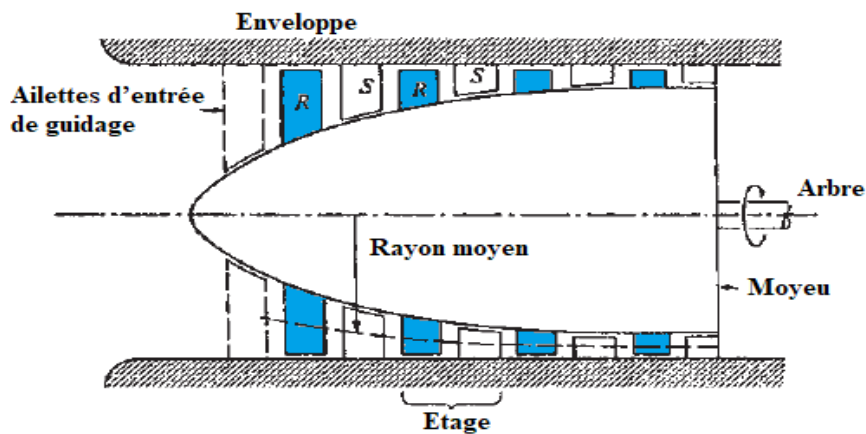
Turbomachine axiale, vue méridionale rangée d'aubes mobile (rotor) et fixes (stator)
